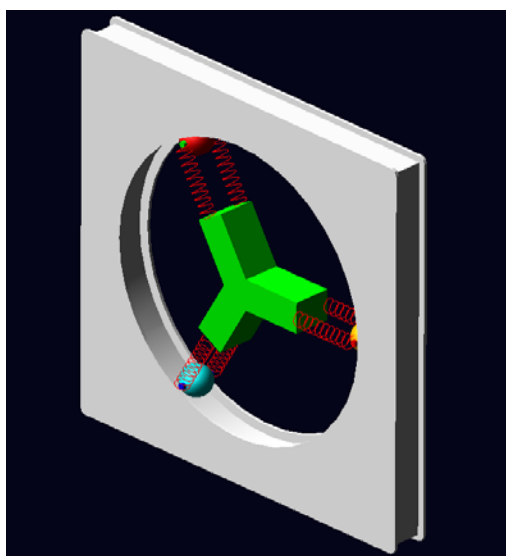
Vista isométrica del rodamiento de 3 bolas
